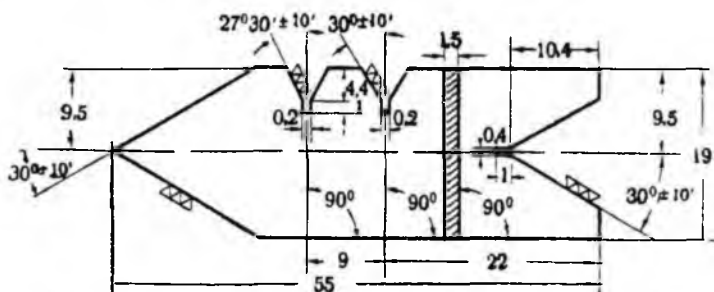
Шаблон для метрической и дюймовой резьбы.
